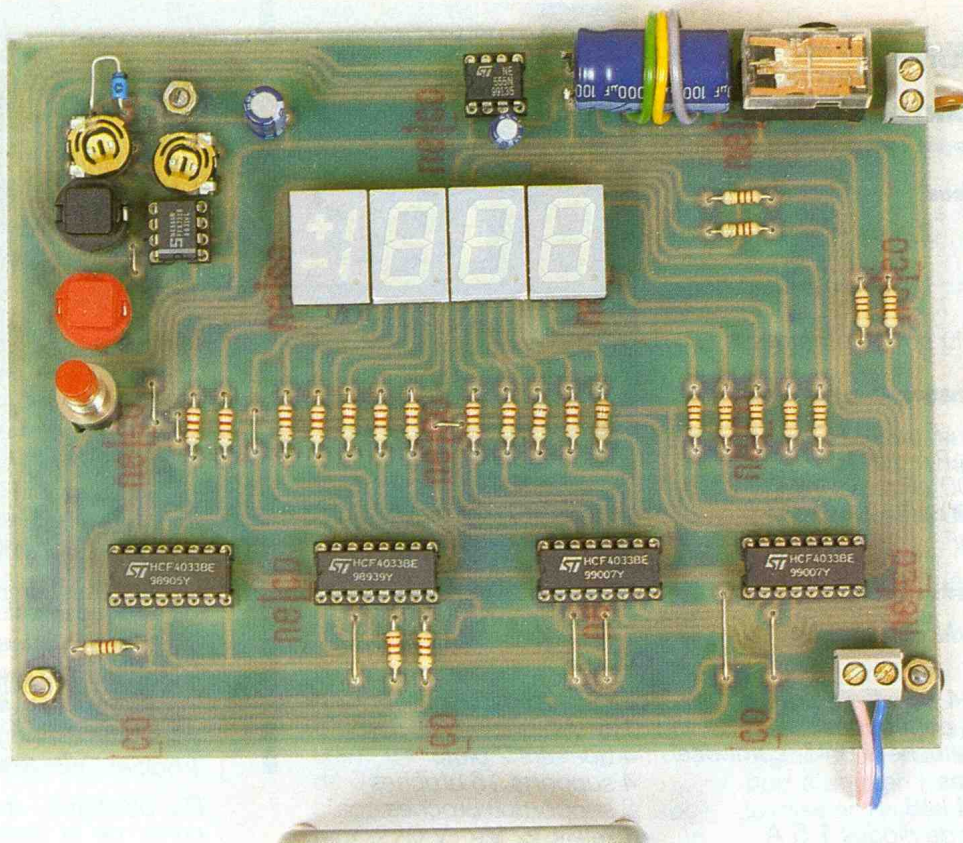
Vue d'ensemble sur le montage prêt à l'emploi.
